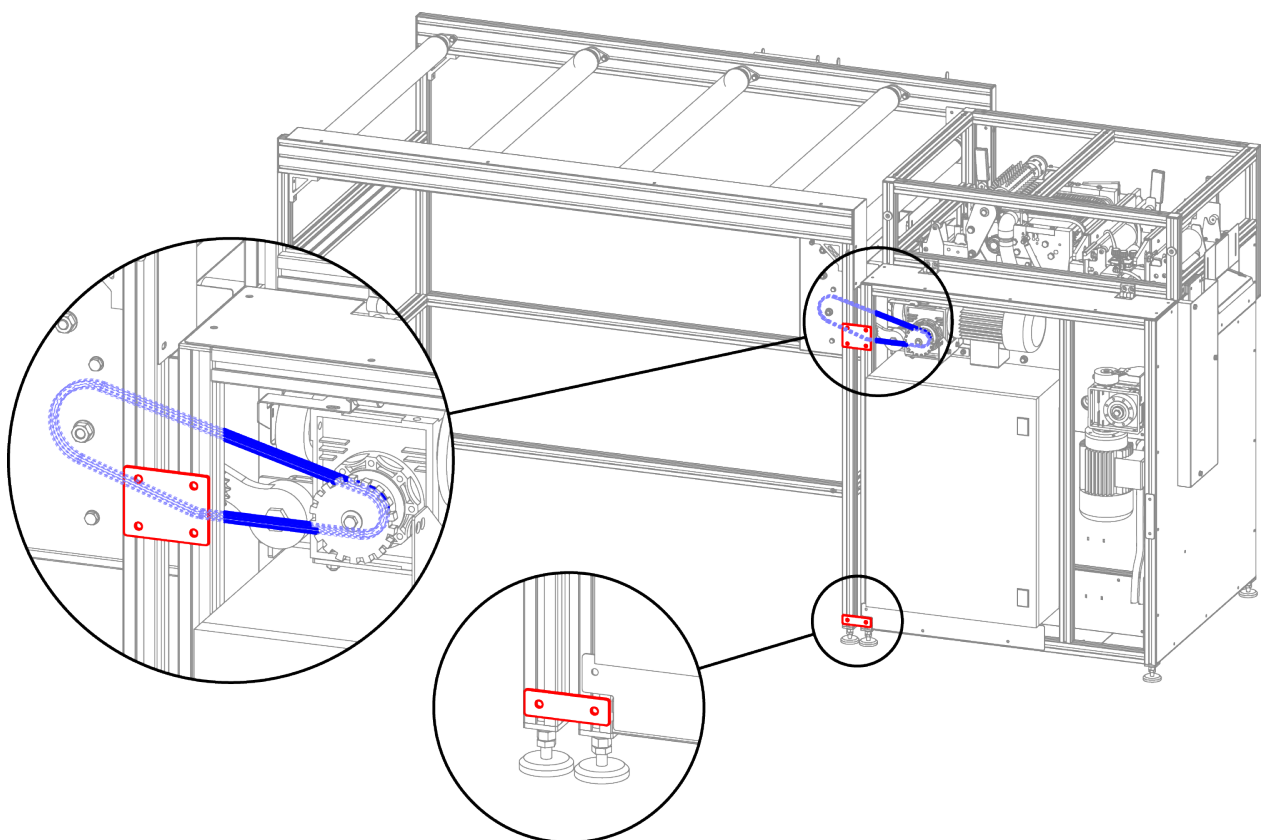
Fissaggio delle piastre di collegamento e installazione della catena
